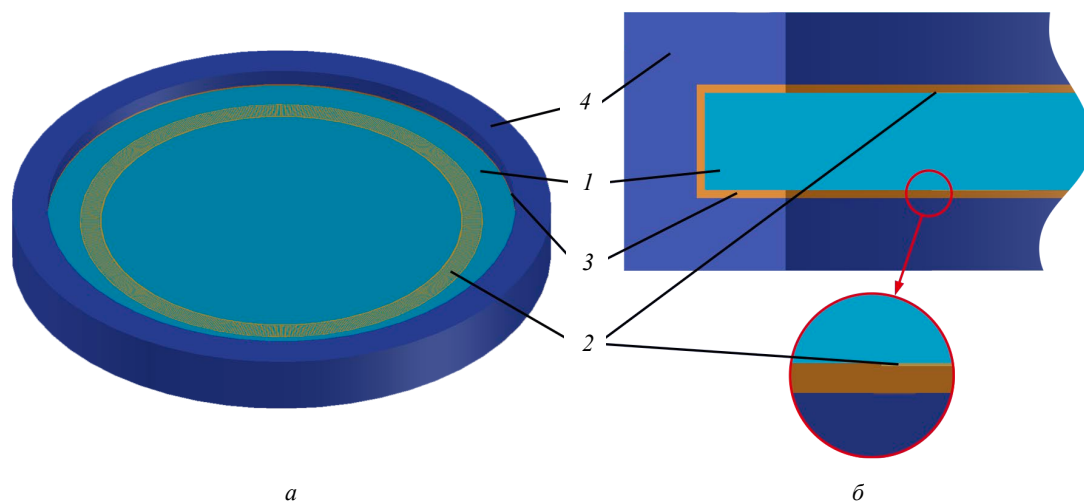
Конструкция чувствительного элемента на поверхностных акустических волнах: а – общий вид; б – вид спереди (1 – консоль; 2 – встречно-штыревой преобразователь; 3 – силиконовый клей; 4 – корпус)
